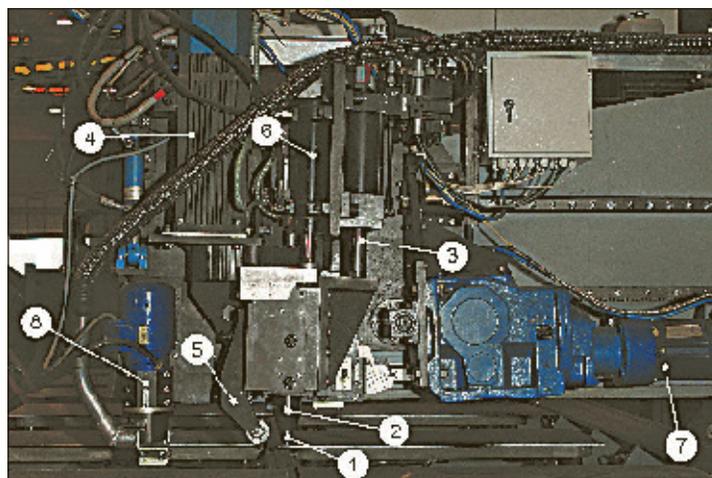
Консоль установки сварки трением с перемешиванием: 1 — инструмент; 2 — шпиндель; 3 — гидроцилиндр подачи шпинделя по оси Z; 4 — электродвигатель привода шпинделя; 5 — прижимной ролик; 6 — гидроцилиндр подачи ролика; 7 — привод подачи по оси Y; 8 — электрошпиндель. Электроприводы вращения шпинделя и перемещения по осям X, Y выполнены на основе серийных приводов компании КЕВ с синхронными двигателями
